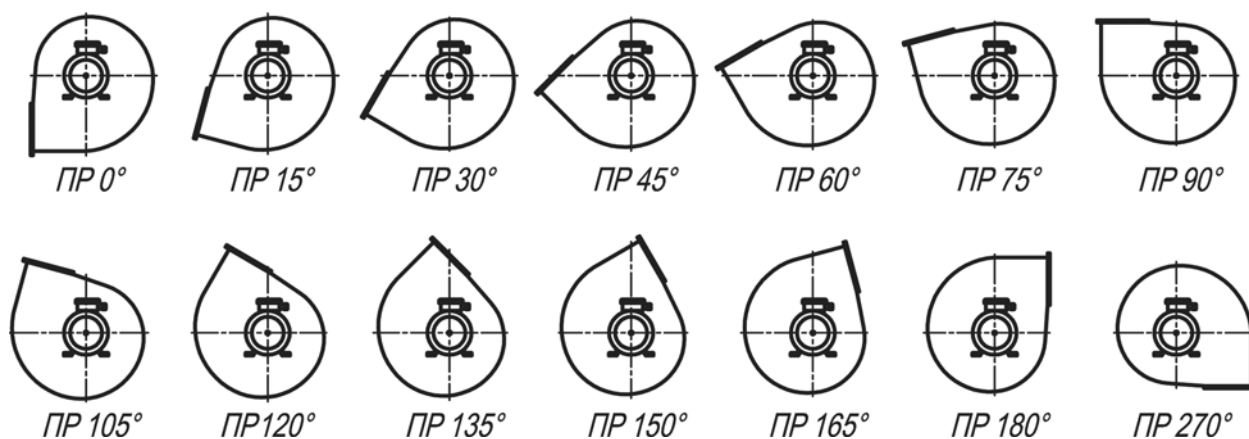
Положение корпуса тягодутьевых машин типа ВД и Д.
